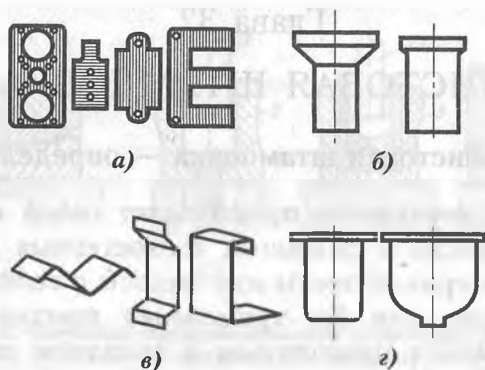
Листовые штампованные детали, полученные вырубкой и пробивкой (а); отбортовкой (б); гибкой (в); вытяжкой и формовкой (г)
